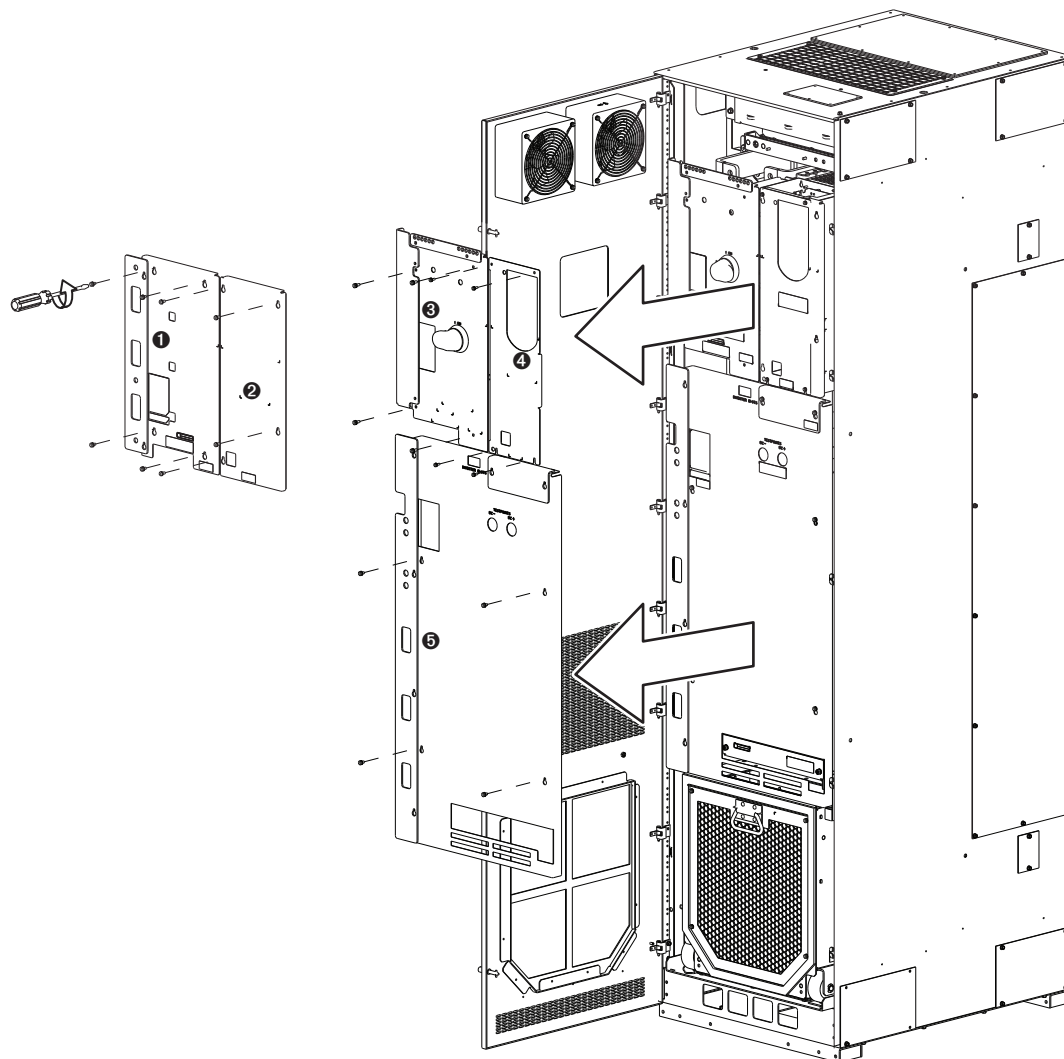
Дверца доступа шкафа типоразмера 8 и более (все типы корпусов)
